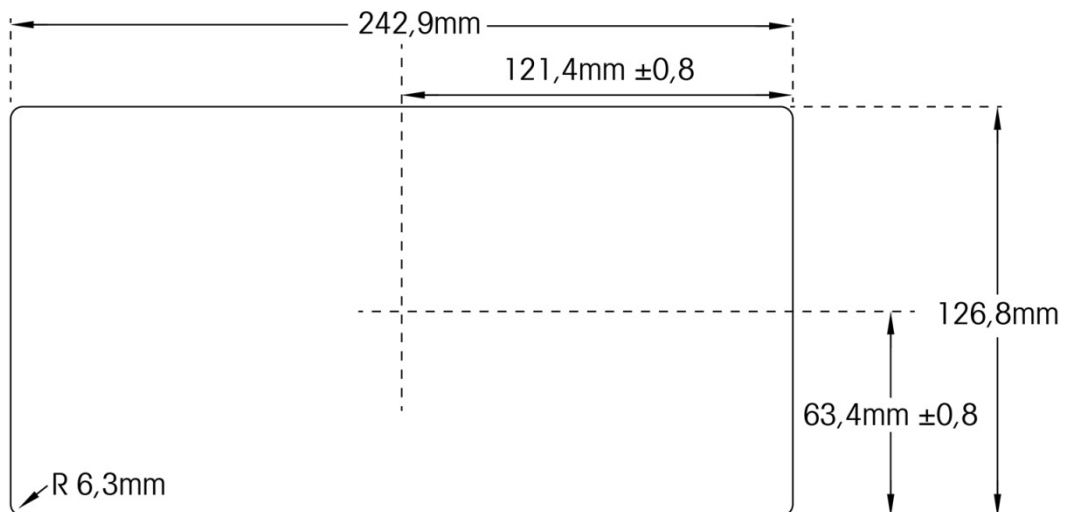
Abmessungen der Aussparung für die IND570-Frontplattenversion
